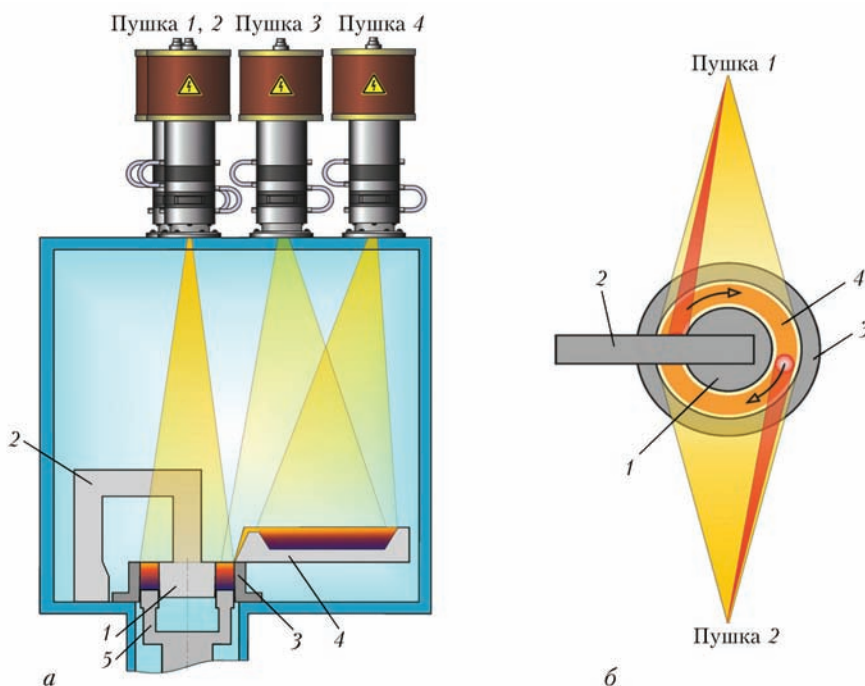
Схемы конструкции кристаллизатора для получения трубчатой заготовки способом ЭЛП (а) и нагрева ванны расплава двумя электронными пушками с развертками лучей в форме полуколец (б, вид сверху): 1 — водоохлаждаемый дорн; 2 — траверса; 3 — водоохлаждаемый тигель; 4 — промежуточная емкость; 5 — водоохлаждаемый шток с заправкой
